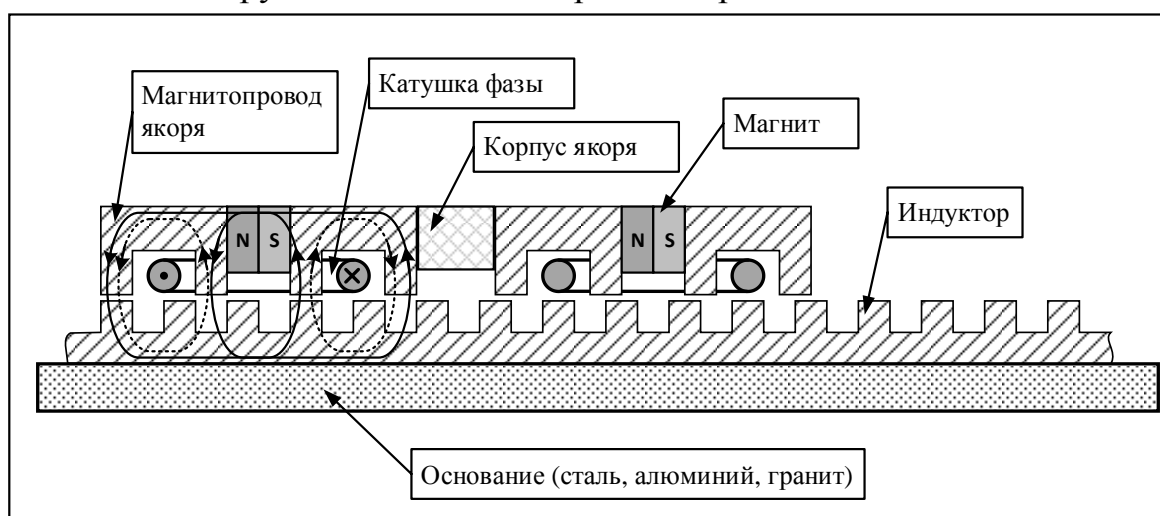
Возможная конструкция линейного индукторного двигателя
